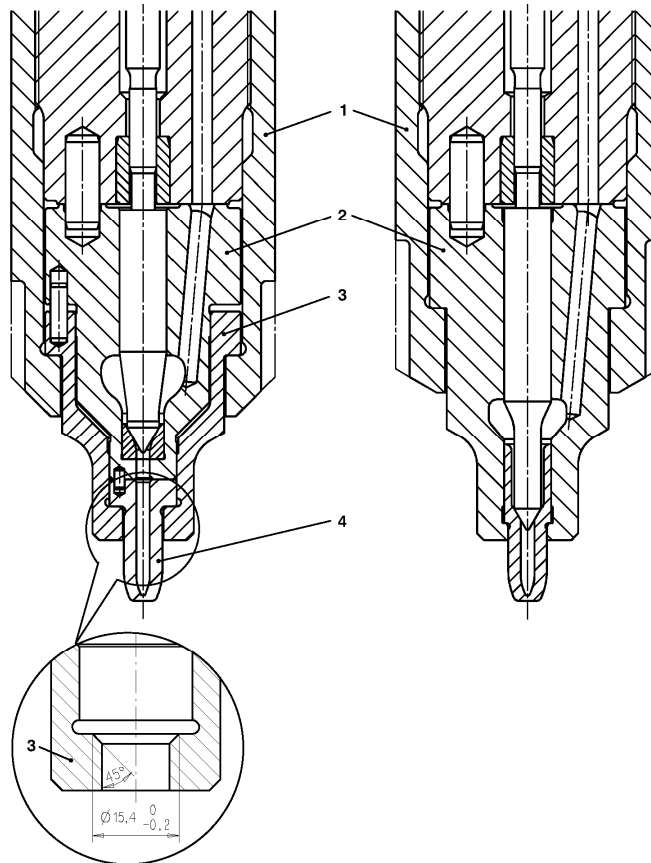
Конструкція стандартного розпилювача (ліворуч), та розпилювача зі зменшеним об’ємом підголкового простору (праворуч): 1 – корпус форсунки; 2 – корпус розпилювача; 3 – додатковий корпус; 4 – змінний наконечник
